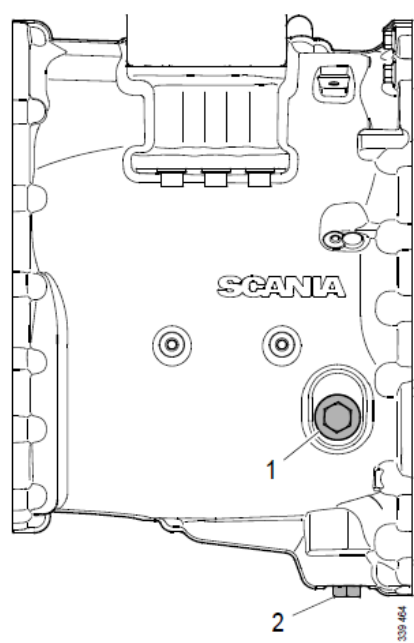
4.-Tapones de drenaje y llenado de caja.
